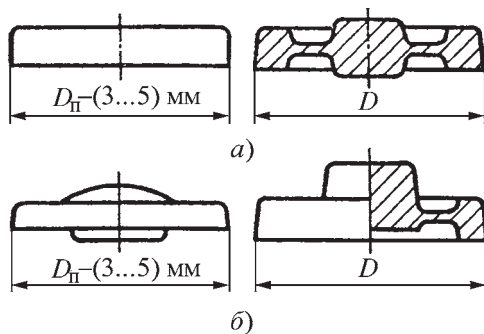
Переходы штамповки поковки типа ступицы с диском и ободом
